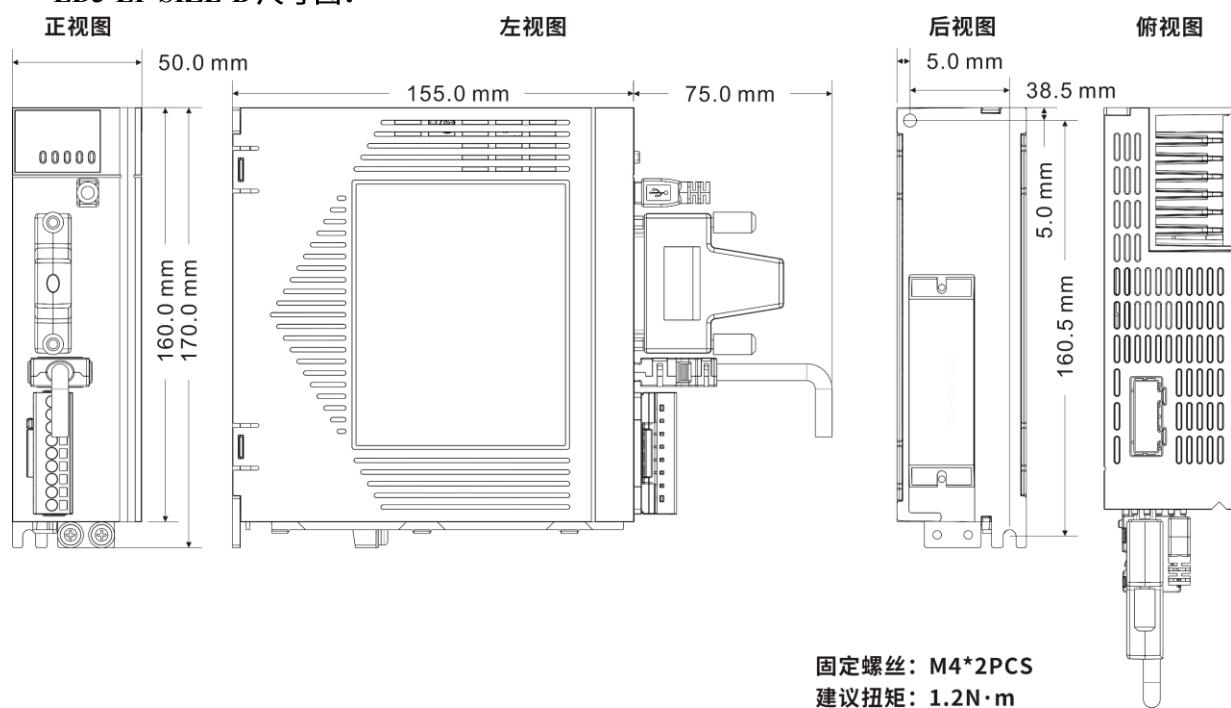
LD3-LP SIZE-B 外形尺寸图 ((单位 mm)
